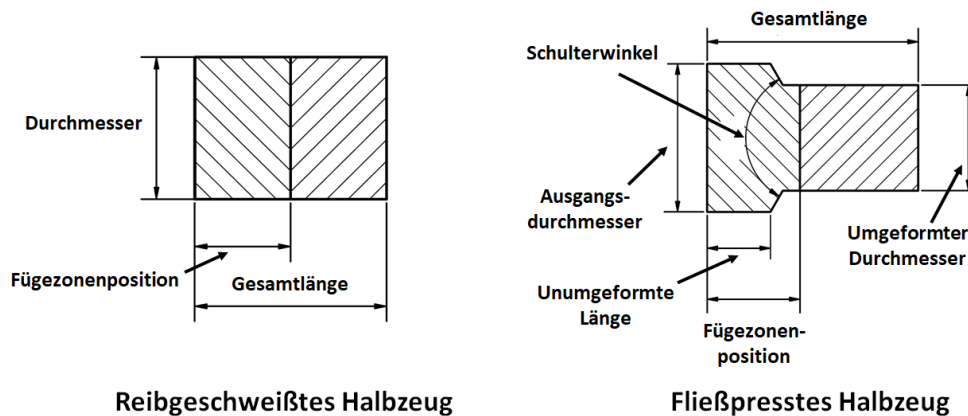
Parametrisierung des reibgeschweißten (links) und des fließpressten (rechts) Halbzeugs
